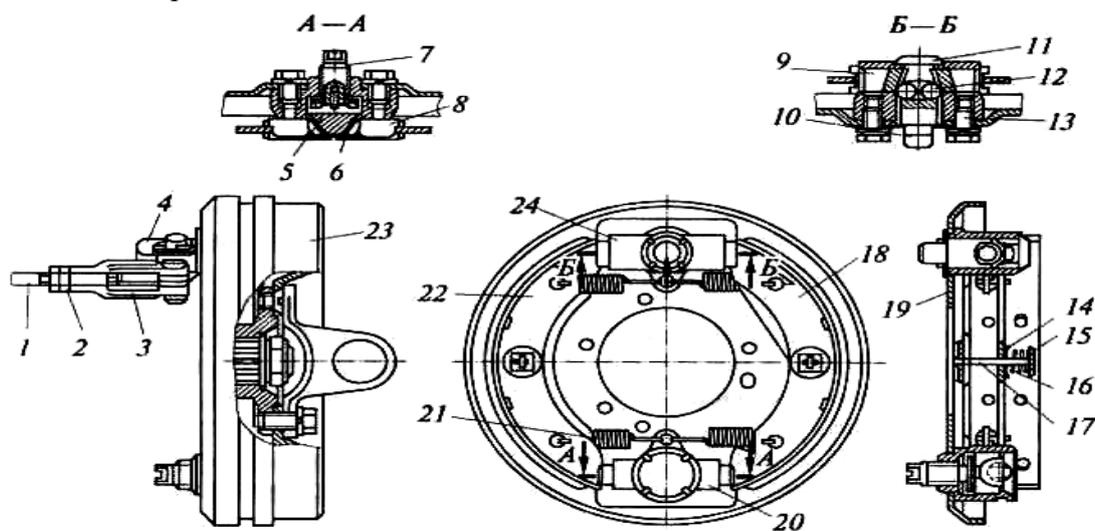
Трансмиссионный стояночный тормоз: 1—тяга привода; 2 — контргайка; 3 — регулировочная вилка; 4 — рычаг привода; 5 — разжимной сухарь; 6 — заглушка; 7 — регулировочный винт; 8 — опора колодки; 9 — толкатель разжимного механизма; 10 — ; 11 — колпак; 12 — шарик разжимного механизма; 13 — болт; 14, 15 — чашки пружины; 16 — пружина; 17 — стержень; 18, 22 — тормозные колодки; 19 — тормозной щит; 20 — корпус регулировочного механизма; 21 — стяжная пружина колодок; 23 — 24 — корпус разжимного механизма
